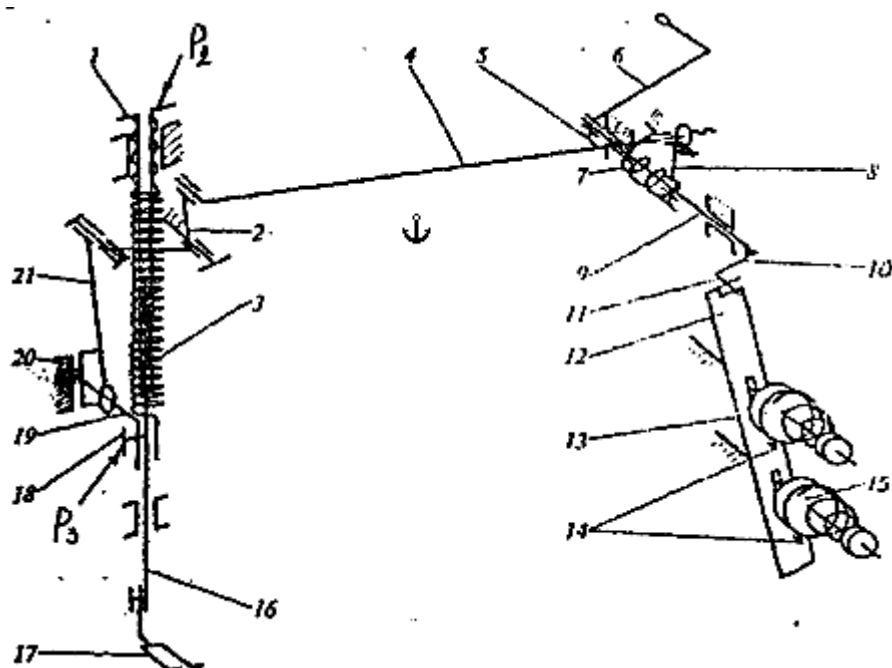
Кинематическая схема узла прижимной лапки швейной машины класса 1276
